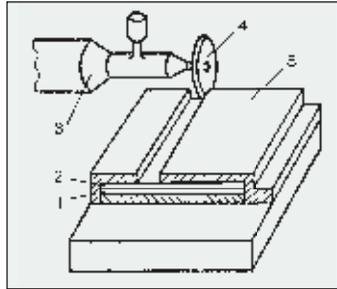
Схема роликовой СТ: 1, 2 — свариваемые заготовки; 3 — шпиндель; 4 — вращающийся ролик; 5 — прижимы
